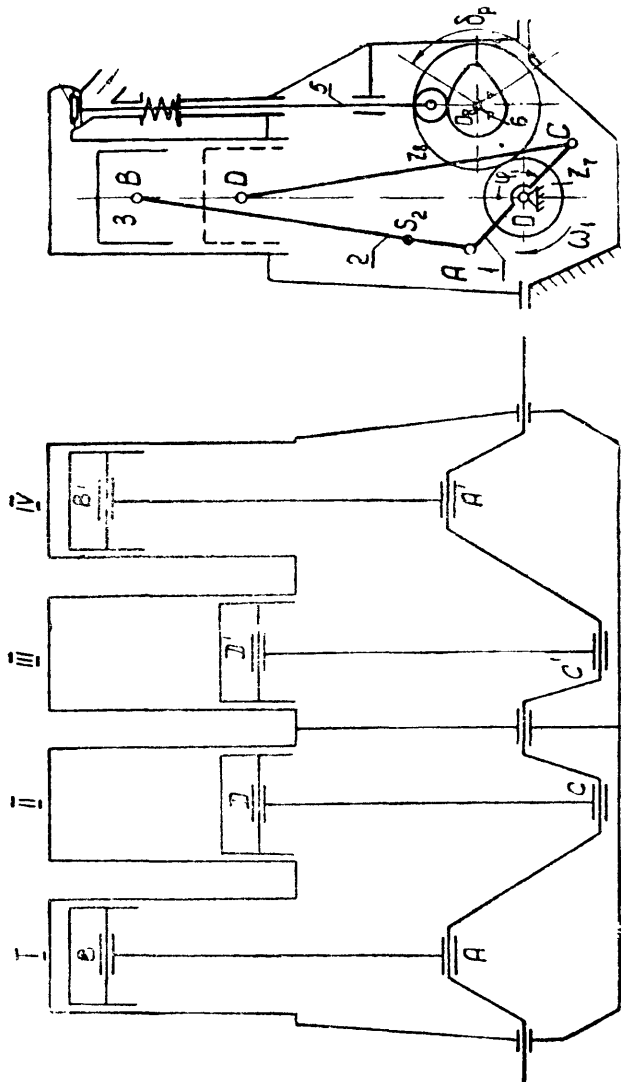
3. Схема механизма двигателя и кулачкового привода клапанов
